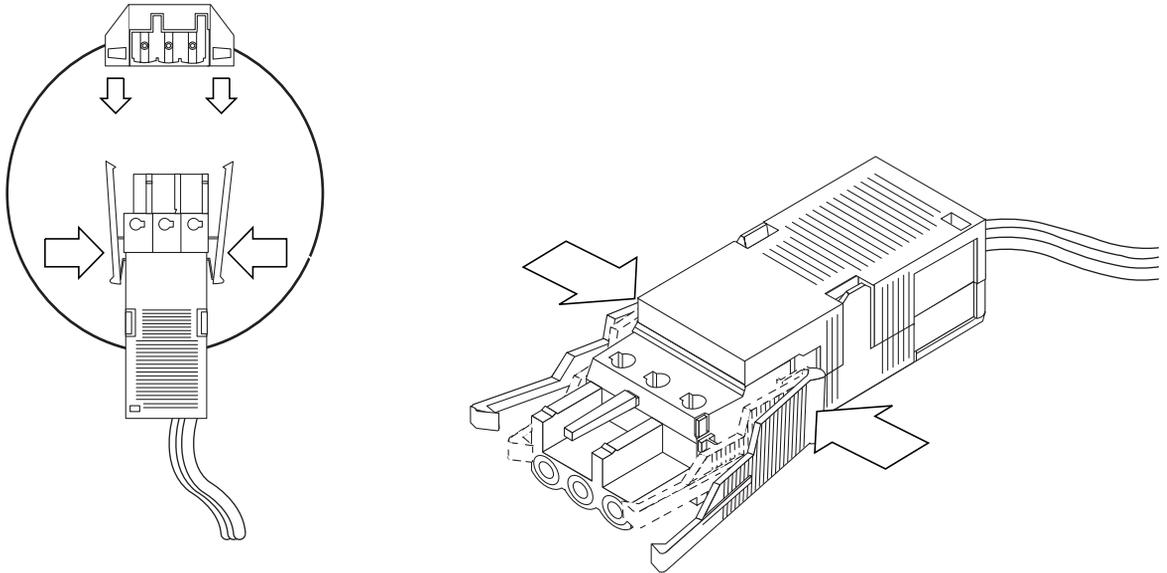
Scollegamento del cavo di alimentazione CC in ingresso dal connettore CC
